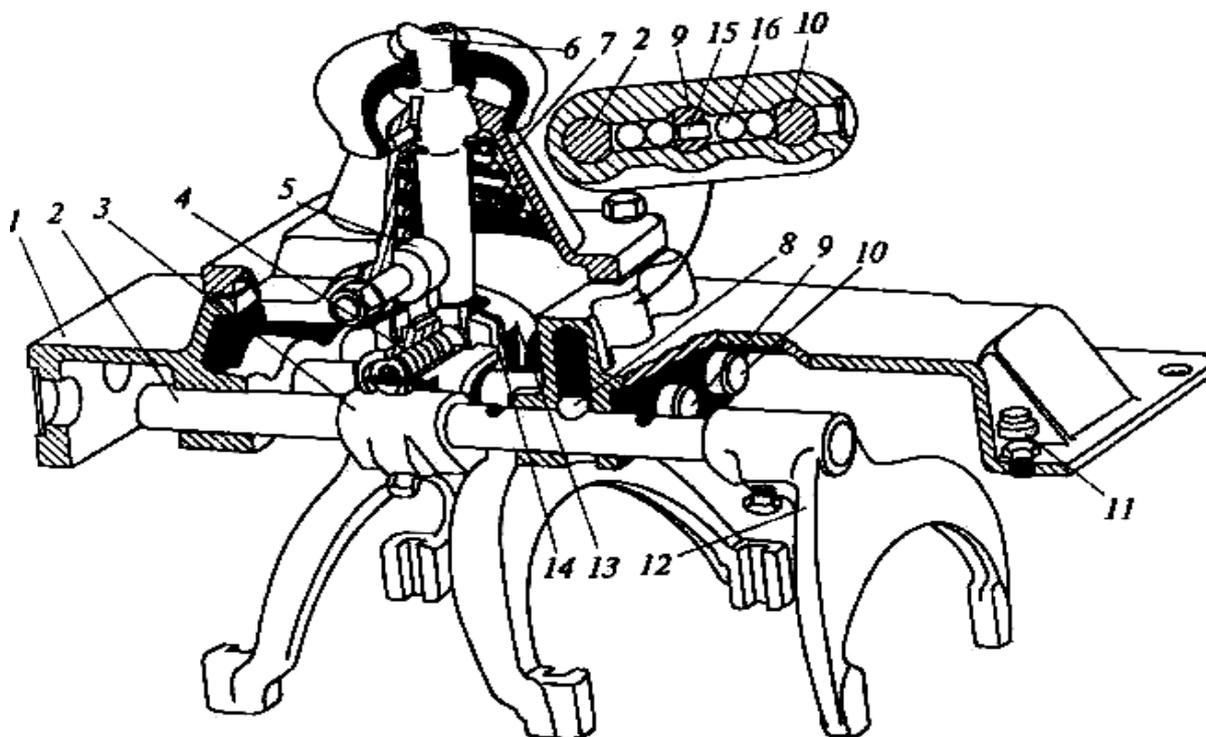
Механизм управления коробкой передач: 1 — крышка картера коробки передач; 2 — ползун включения I передачи и заднего хода; 3 — головка ползуна; 4 — пружина предохранителя включения заднего хода; 5 — промежуточный рычаг включения I передачи и заднего хода; 6 — рычаг переключения передач; 7 — корпус рычага переключения; 8 — шарик фиксатора; 9 — ползун включения IV и V передач; 10 — ползун включения II и III передач; 11 — сапун для сообщения картера коробки передач с атмосферой; 12 — вилка включения I передачи и заднего хода; 13 — вилка включения II и III передач; 14 — вилка включения IV и V передач; 15 — штифт замка ползунув; 16 — шарик замка ползунув
